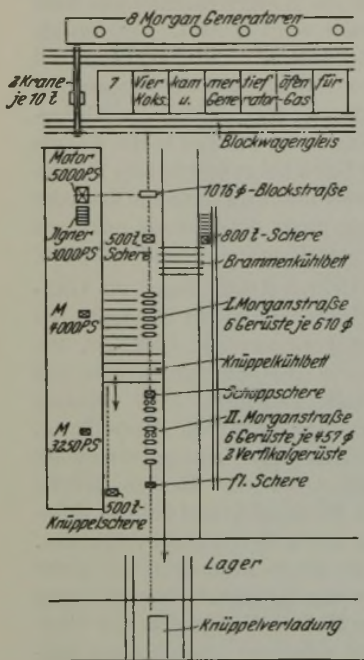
Lageplan eines amerikanischen Walzwerkes.
